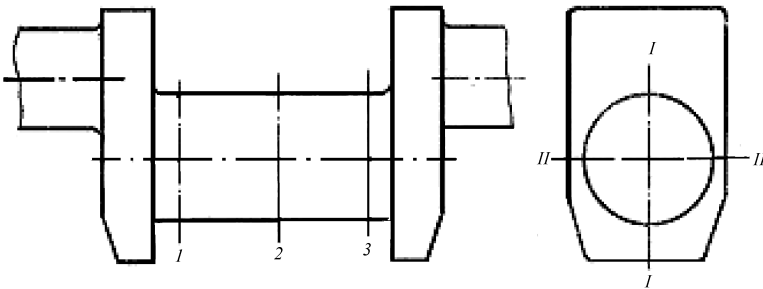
Місця вимірювання шийки колінчастого вала
